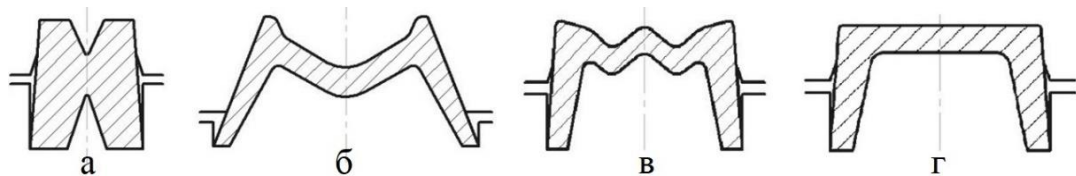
Виды калибров, применяемых в прямополочном типе калибровки: а – разрезной калибр 2121; б, в – формообразующие калибры 3221,4131; г – чистовой калибр 1132
